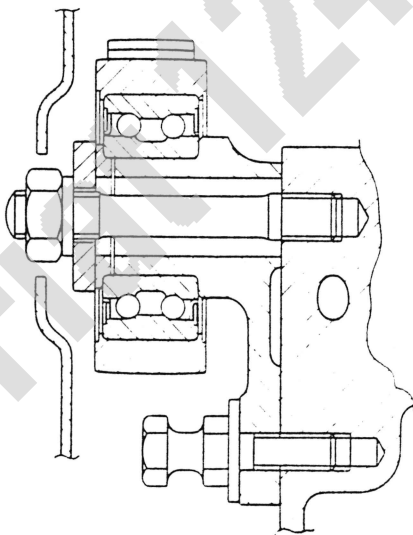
Schnitt des Spanners mit Feder, zum Spannen des Steuerriemens.
